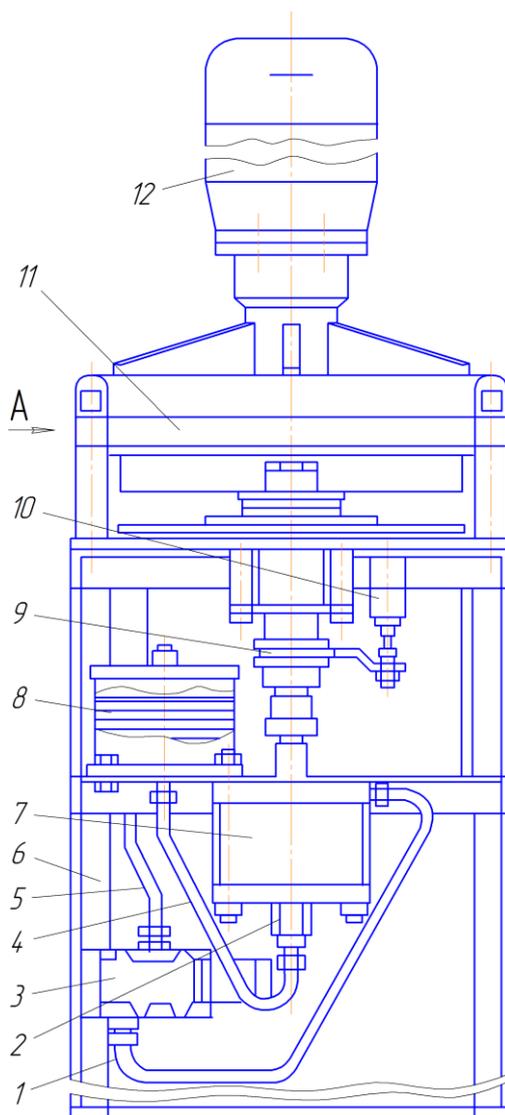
Устройство для обслуживания муфт сцепления
